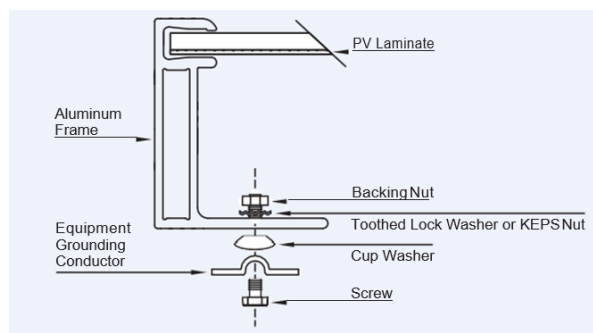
Vue détaillée de l'assemblage de la vis de mise à la terre
